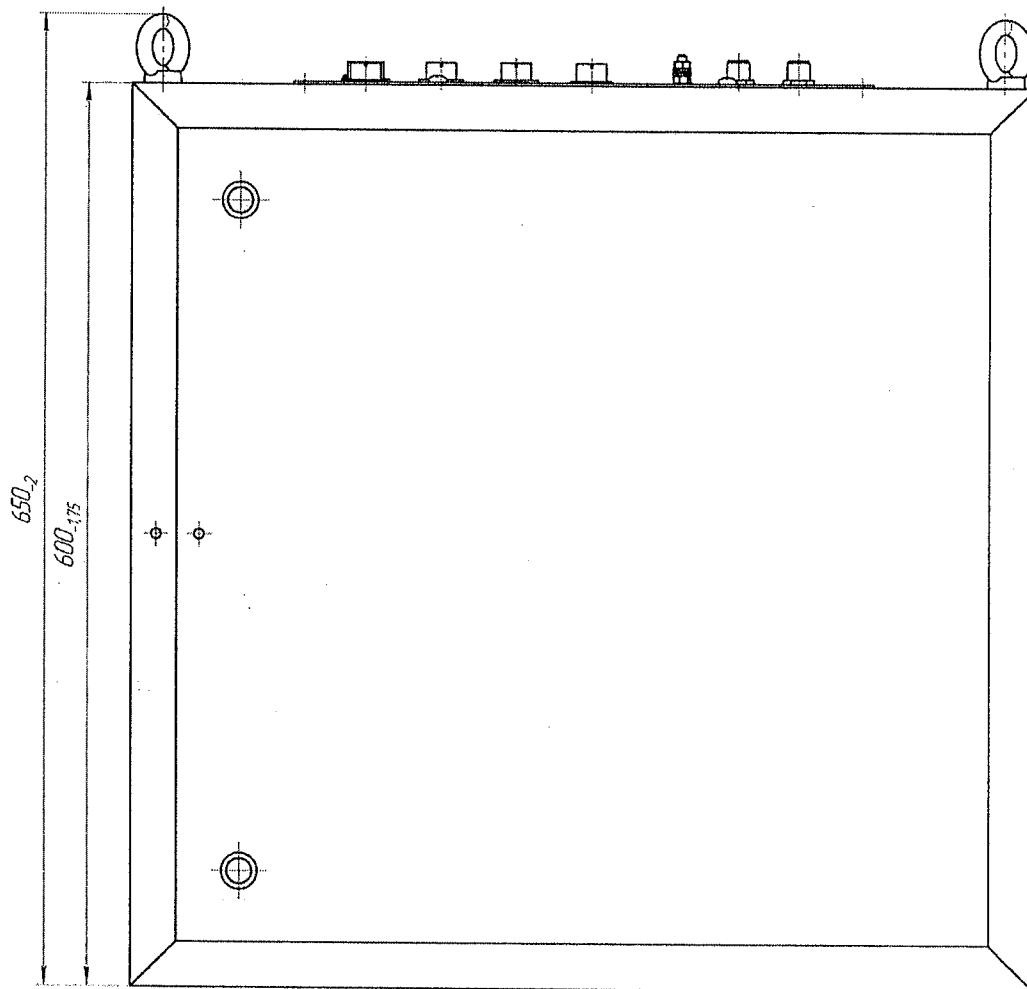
Внешний вид (вид спереди) и габаритные размеры
